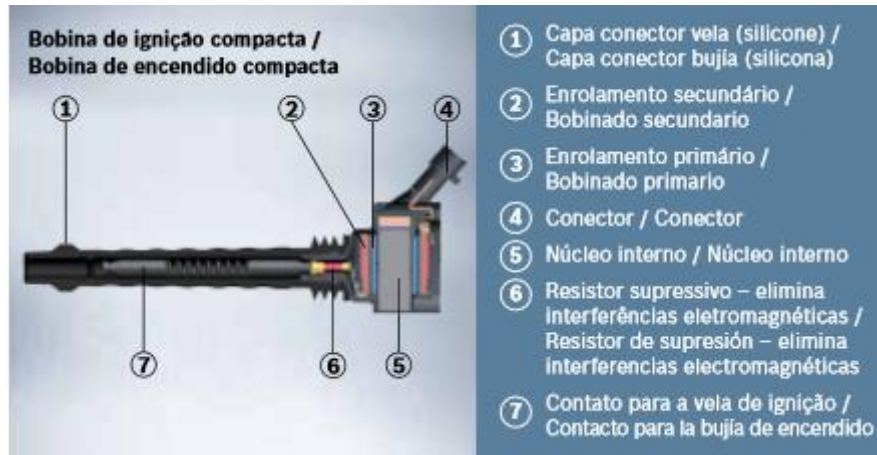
BOBINA DE IGNIÇÃO TIPO CANETA. (BOSCH)
